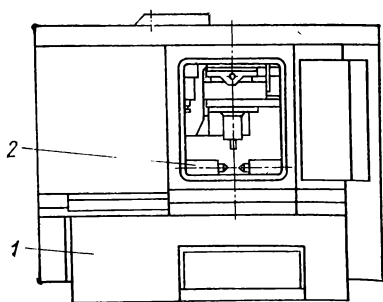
Общий вид зубошевинговального станка, на котором обрабатываемое колесо расположено на неподвижной станине
